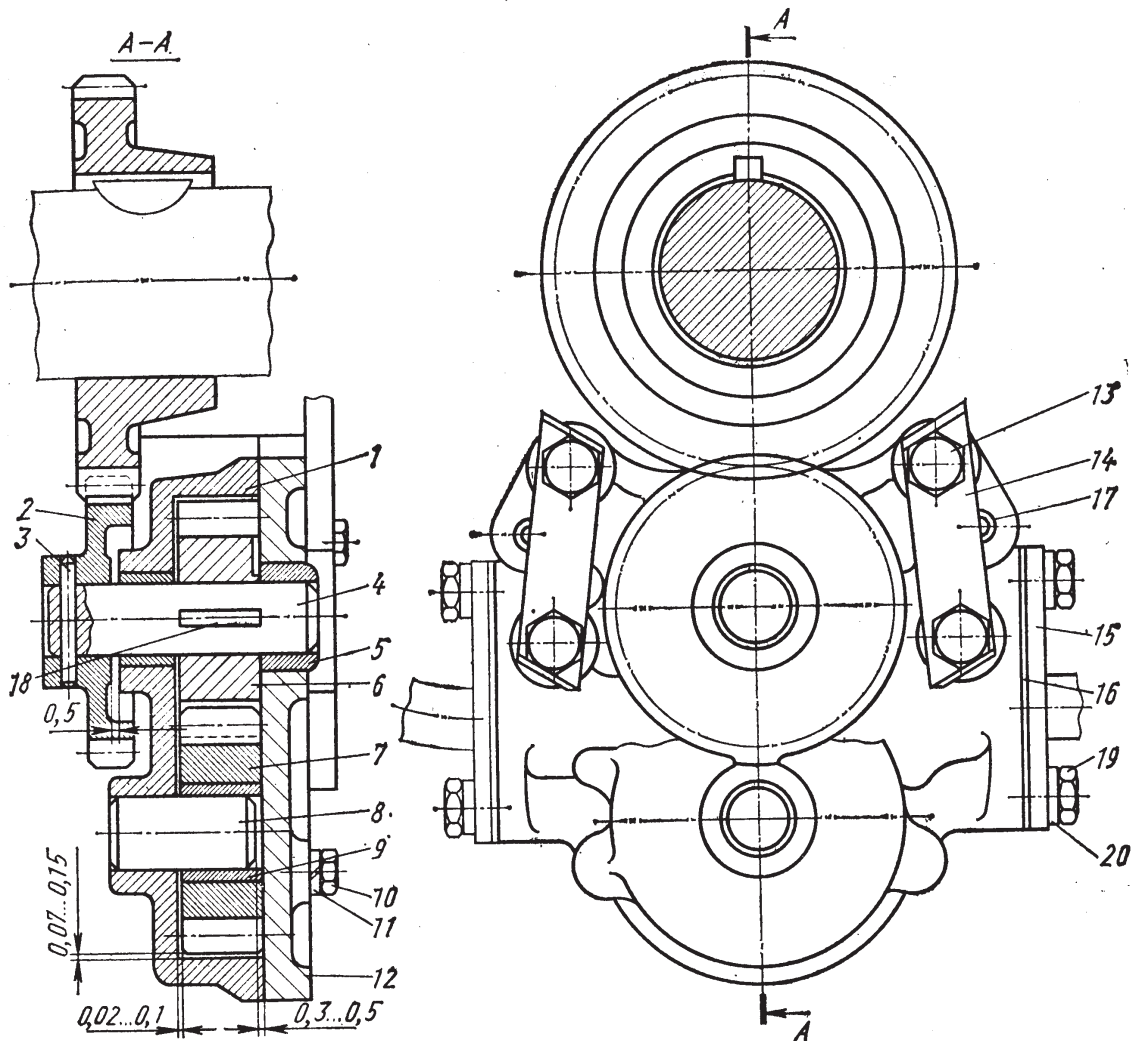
Схема конструкции шестеренного насоса трактора: 1 – корпус, 2 – ведомое зубчатое колесо, 3 – штифт, 4 – валик, 5 – втулка, 6 – зубчатое колесо, 7 – шестерня, 8 – ось, 9 – втулка, 10 – винт, 11 – шайба, 12 – крышка, 13 – болт, 14 – стопорная пластина, 15 – труба приемника, 16 – прокладка, 17 – штифт, 18 – винт, 19 – шайба
